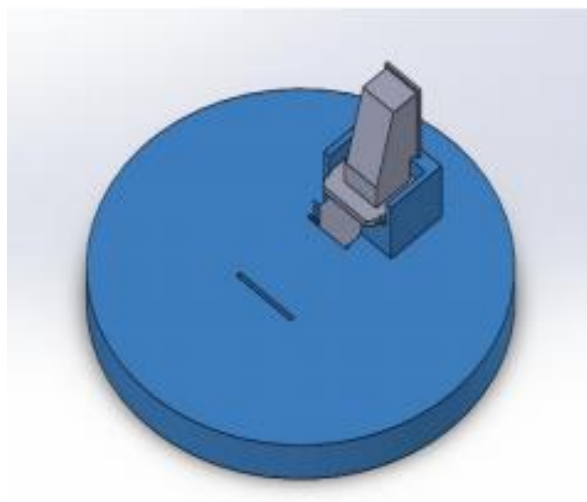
Fixture para operación de soldadura de L Flex, con Detector de Loflo, vista 2.
